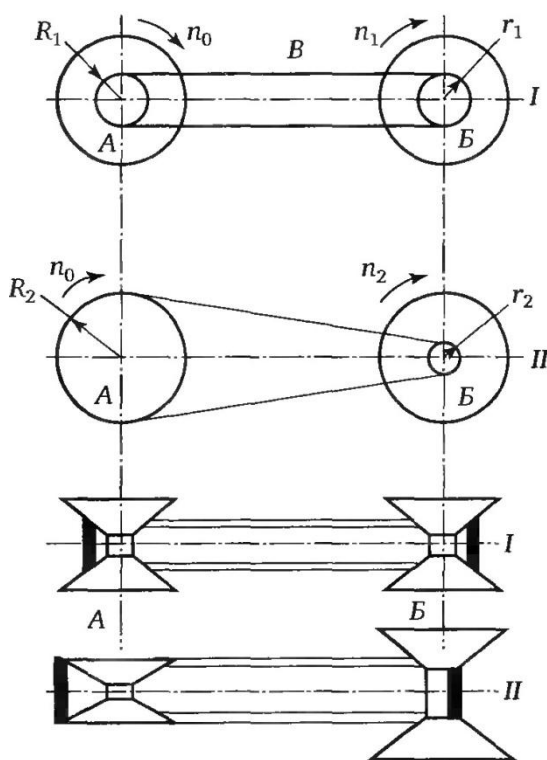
Клиноременный вариатор с раздвижными конусами:
